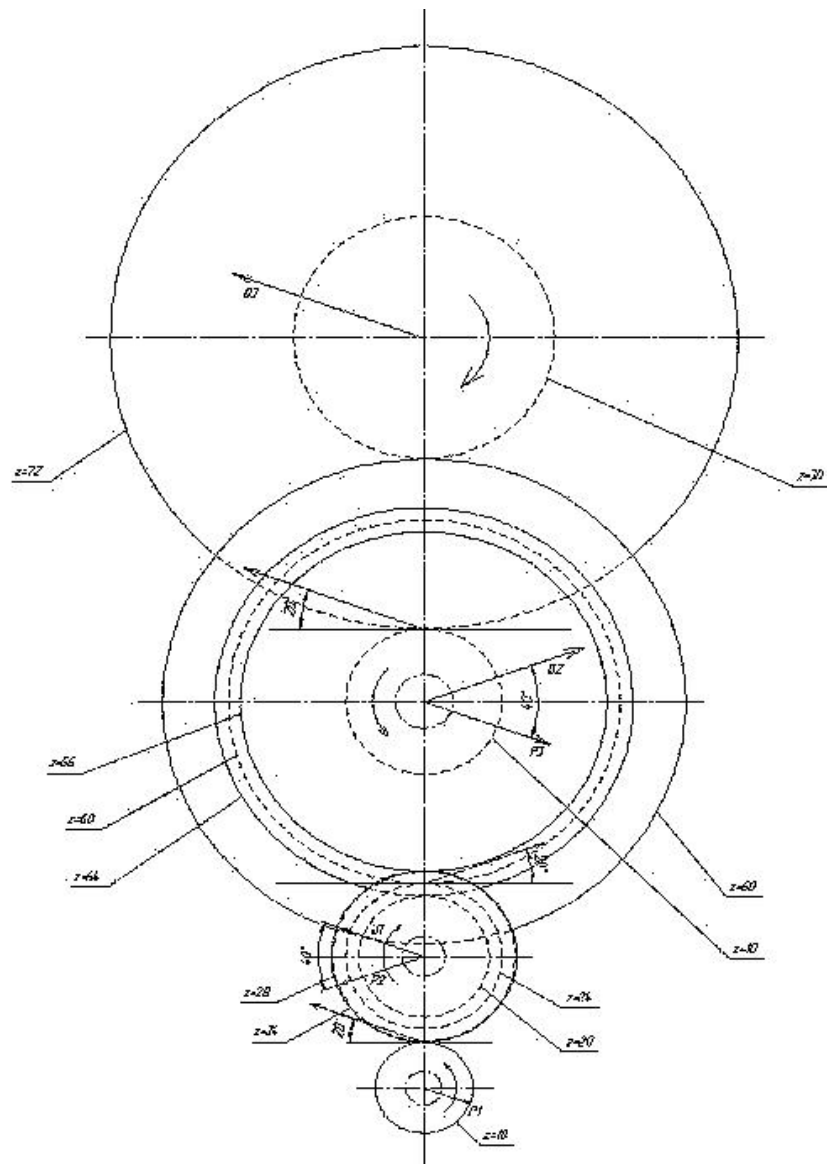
Розрахункова схема згортки коробки швидкостей
